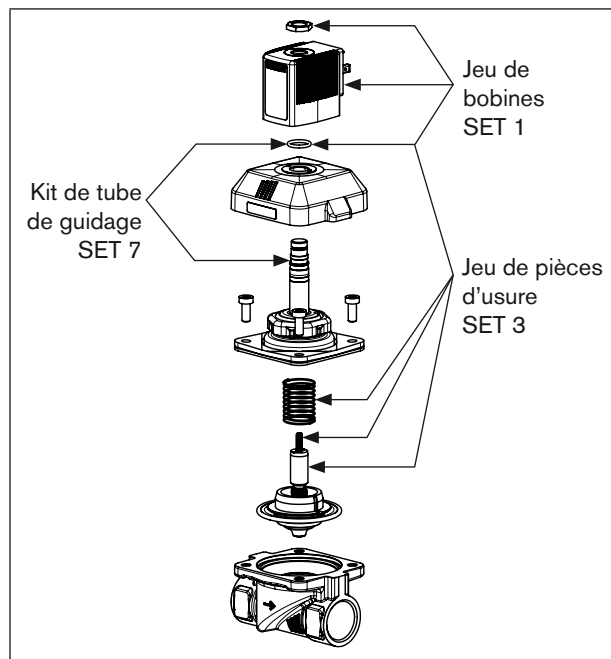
Jeu de pièces de rechange Type 6213 EV
